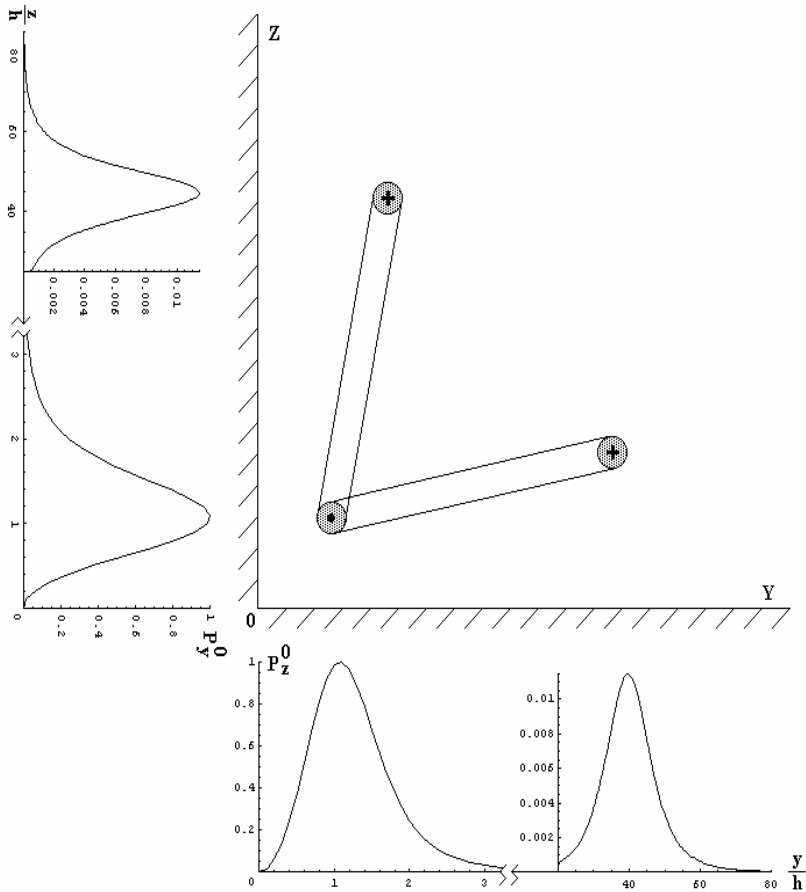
Распределение сил магнитного давления вдоль поверхностей углового изгиба листовой заготовки
